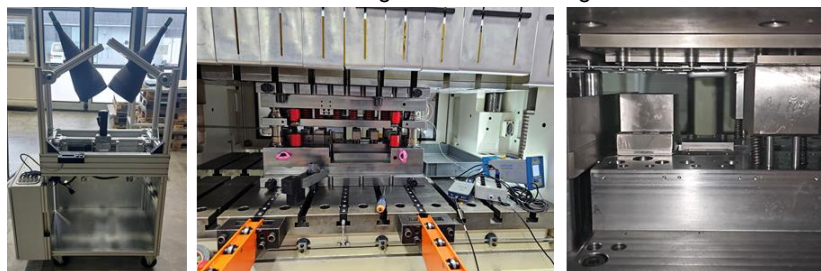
Aufbau des Multi-Axial-Prüfstands mit Stereokamera (l.), eingebautes Versuchswerkzeug (m.) und Blick ins Werkzeug zur optischen Schwingungsüberwachung per Kamera (r.)
